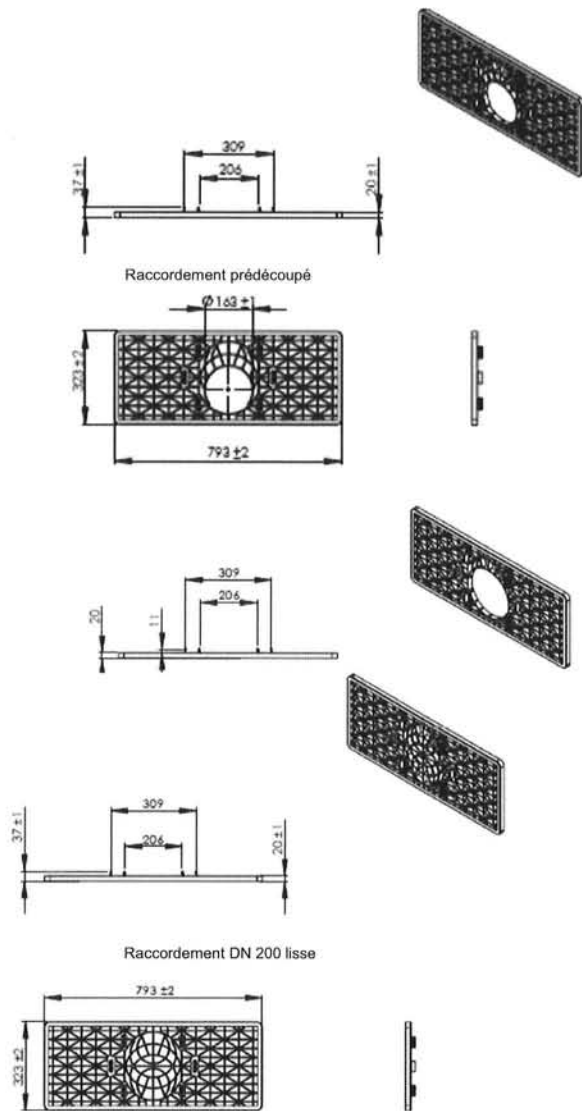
Plaque d'about et plaque d'about ajourée ouverture DN 150 ou DN 200
